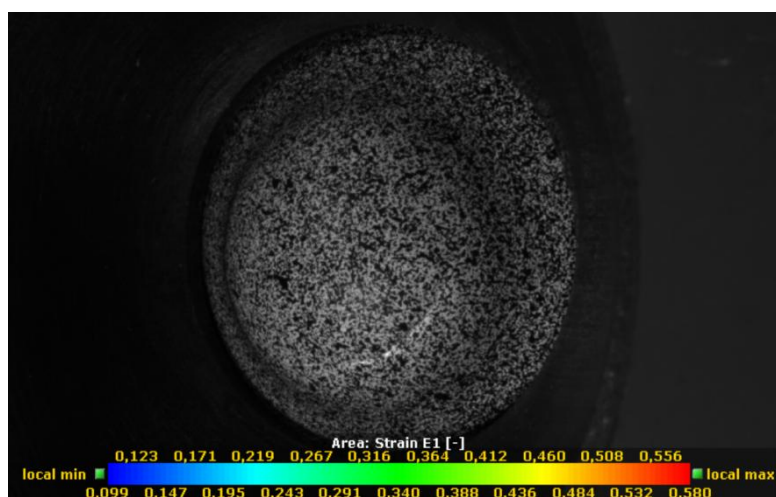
Rozložení deformace uprostřed děje při rychlosti nástroje 50 mm/min.
